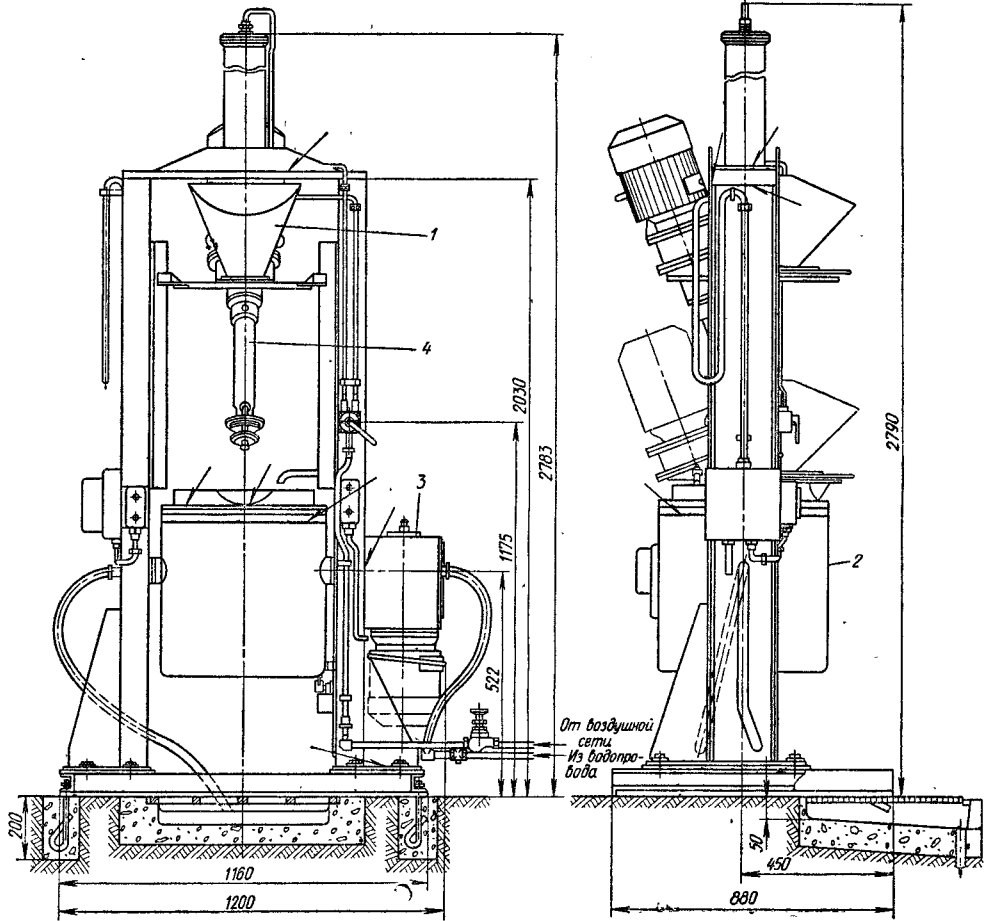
Установка для приготовления огнеупорной обмазки мод. 661:
